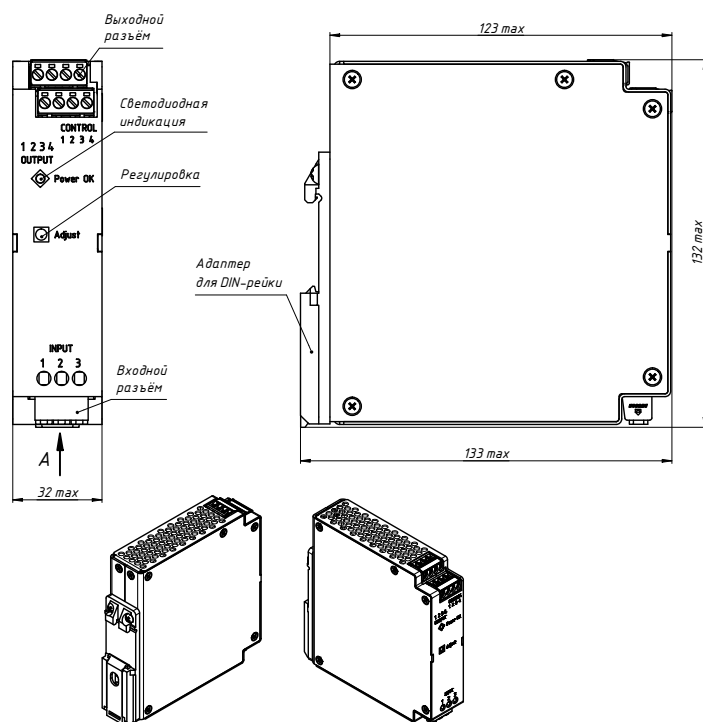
Габаритный чертеж для исполнения VDD75TND.
